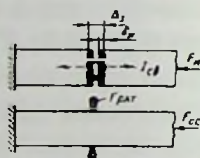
Схема образования соединения при стыковой сварке оплавлением (F_n — начальное усилие; $F_{ос}$ — усилие осадки; Δ_z — зазор между деталями; $\delta_{ж}$ — слой расплавленного металла).
